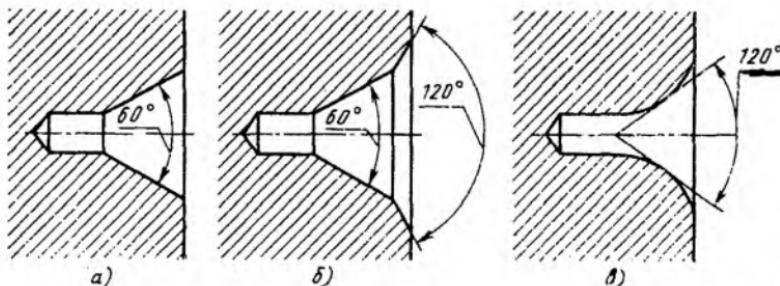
Центровые отверстия без предохранительного конуса (а) с предохранительным конусом (б) и выпуклой образующей (в)
